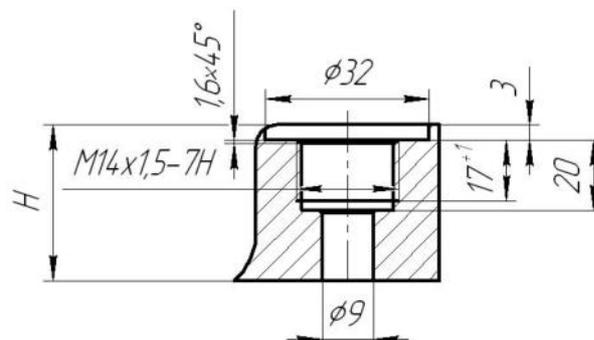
Присоединительные размеры под установку датчиков температуры подшипников (для агрегатов типа К)
